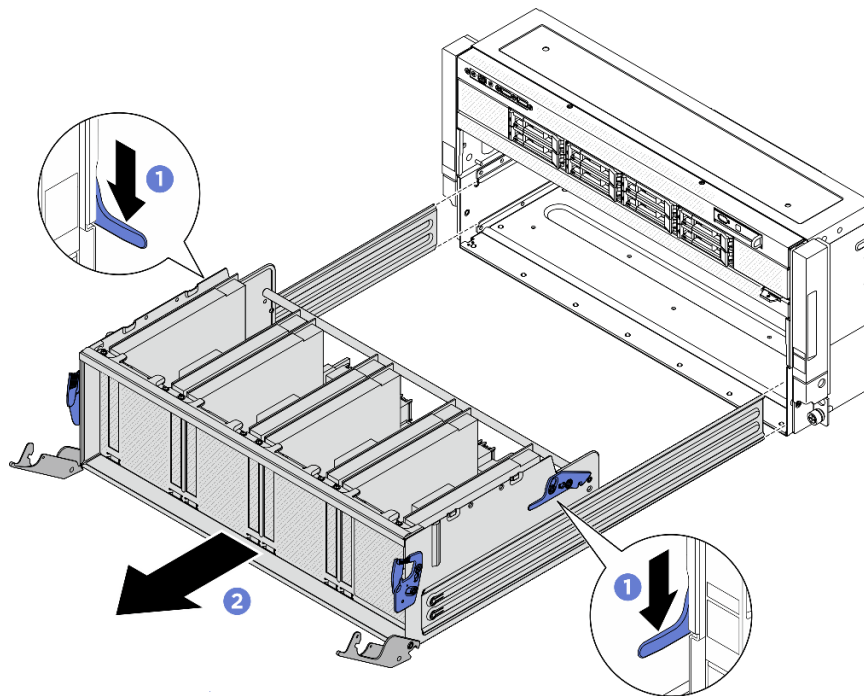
Entfernen des PCIe-Switch-Shuttles
